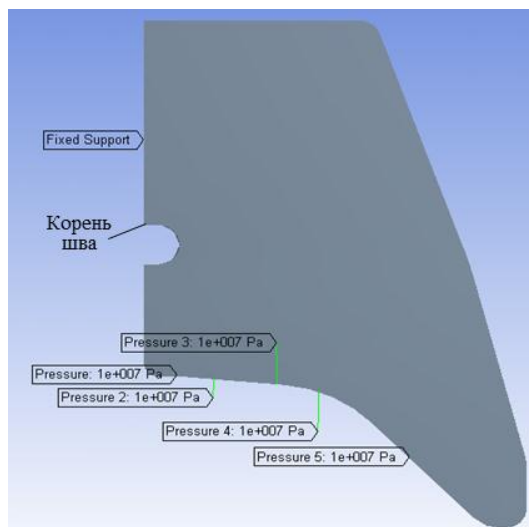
Сечение установочного кольца для электронно-лучевой сварки
